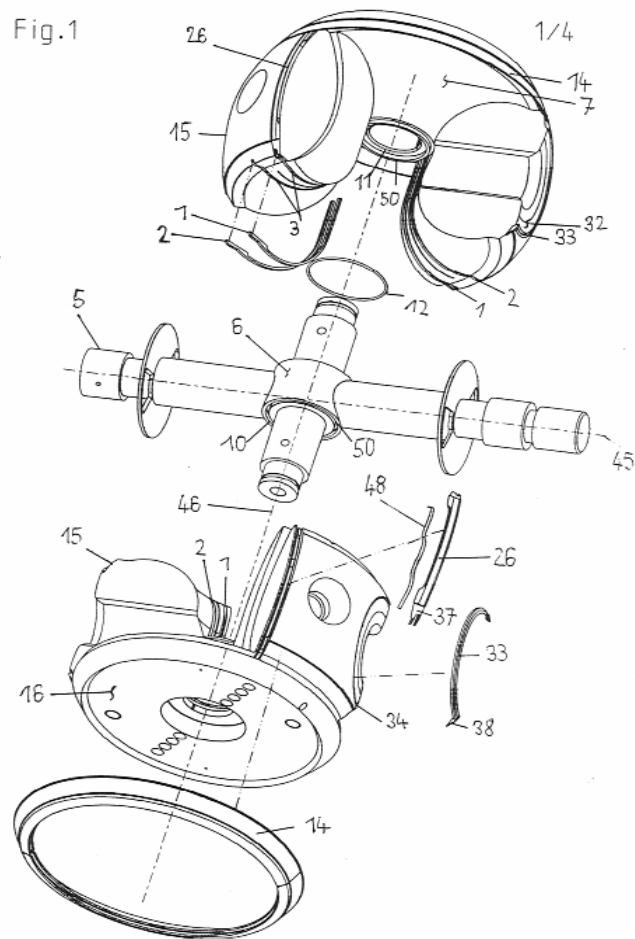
CAD-Explosionszeichnung von Umlauf+Schwenkachse, zweiarmigen Kugelkolben und OBLIQUE-Dichtring- + -Leisten-System mit Wellenfedern (PERAVES-CAD)
